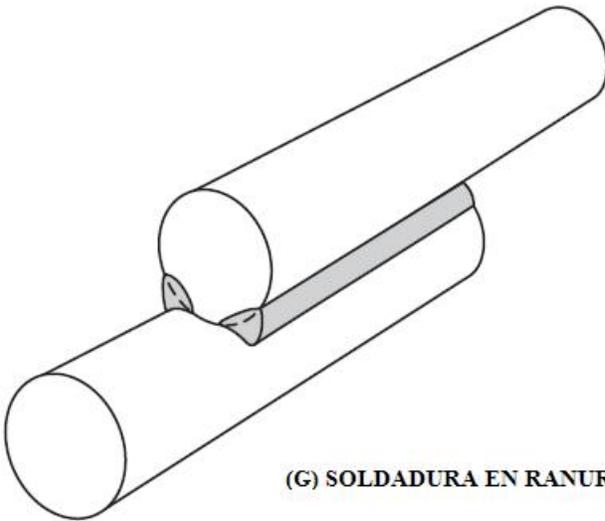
Juntas Soldadas Doble Ranura
